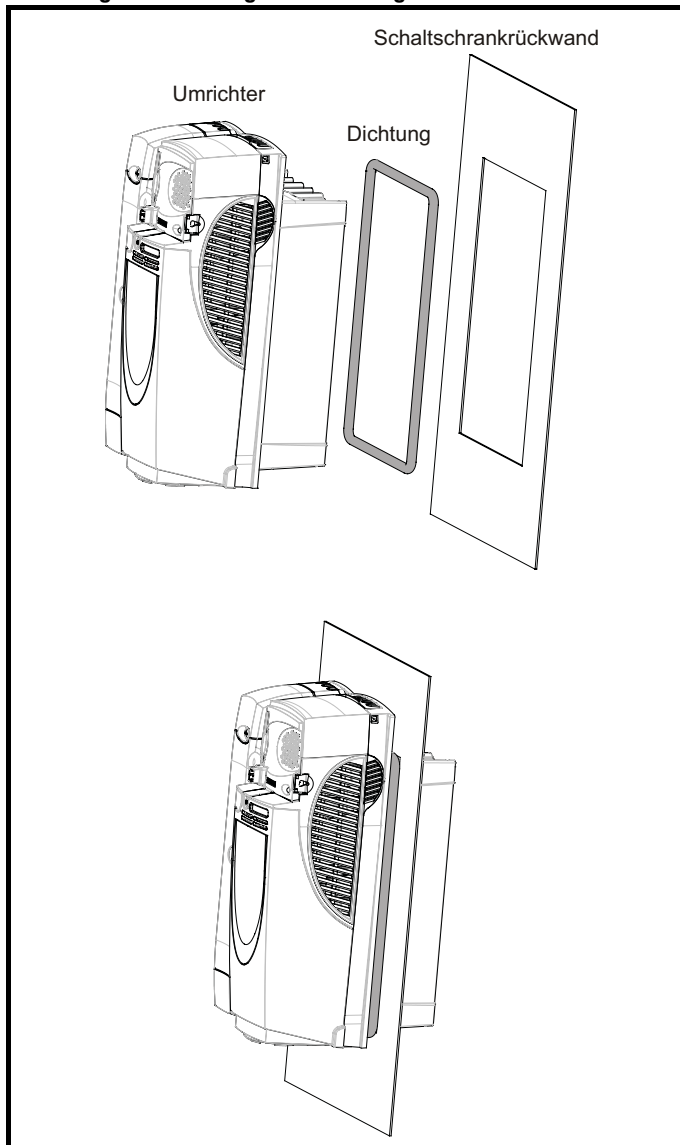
Beispiel einer Durchsteckmontage in IP54-Ausführung (UL Typ 12/NEMA 12)
